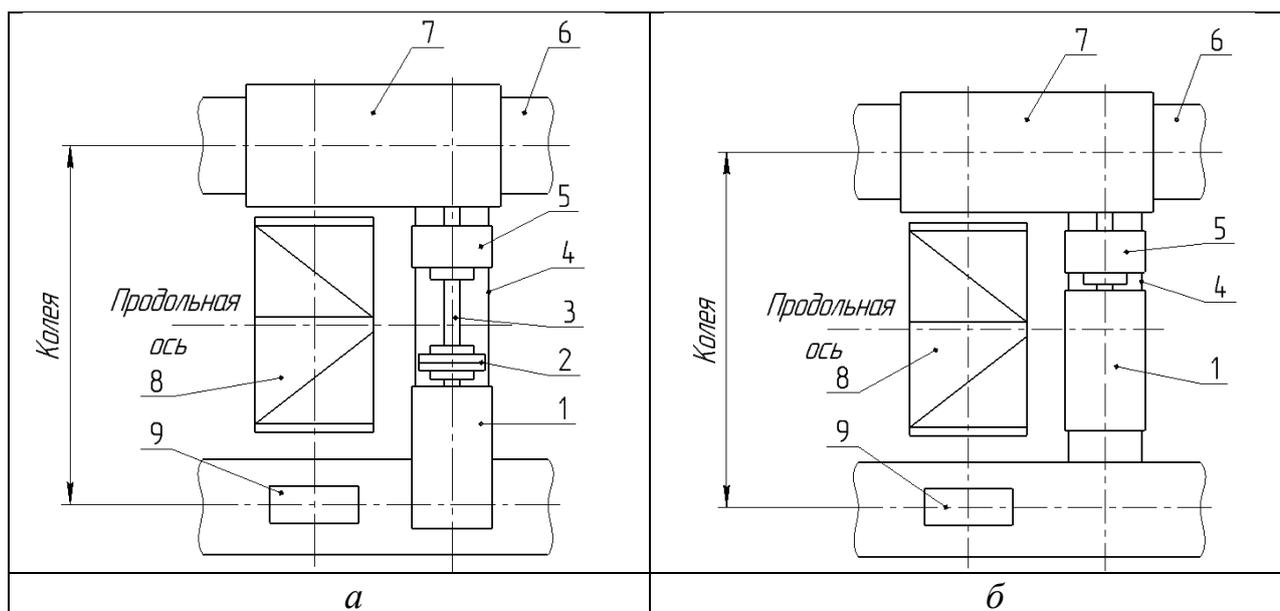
Компонка механизма подъема груза: 1 – двигатель; 2 – упругая муфта; 3 – плавающий вал; 4 – поперечная балка; 5 – тормозная муфта; 6 – продольная балка тележки; 7 – редуктор; 8 – барабан; 9 – внешняя опора барабана
